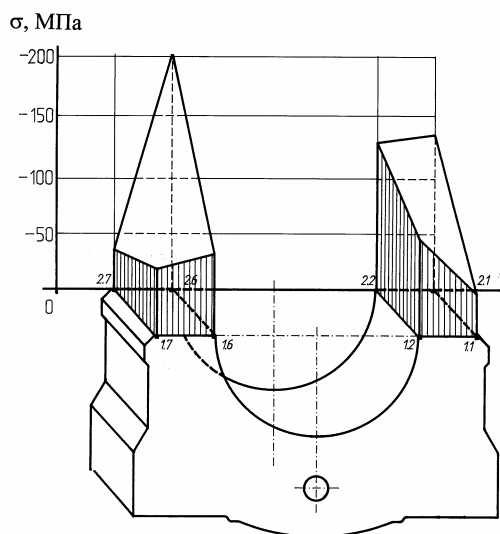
Эпюры напряжений на привалочной поверхности крышки коренной опоры от затяжки болтов
